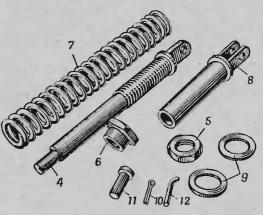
Детали компенсирующего механизма: 4 — стержень; 5 — гайка; 6 — нажимная гайка; 7 пружина; 8 — вилка: 9 — шайбы; 10 — шплиит; 11 ось: 12 - чека
